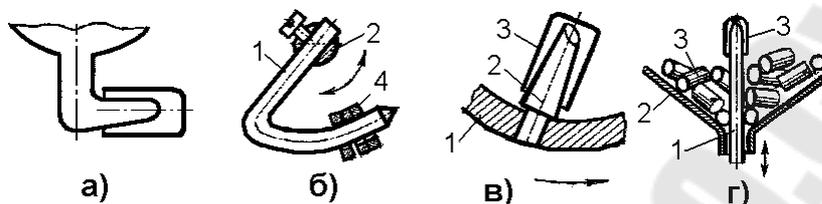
Конструктивные исполнения крючковых и штыревых захватно-подающих механизмов
